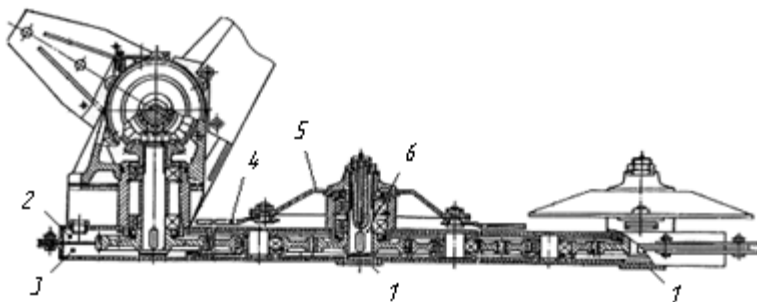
Конструкция многороторного рабочего органа косилки с боковым приводом: 1 – опоры; 2 – верхняя часть корпуса; 3 – нижняя часть корпуса; 4 – нож; 5 – диск; 6 – вал
